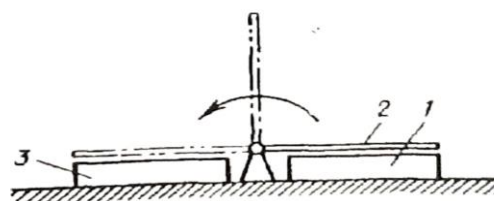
Схема пристрою для складання і зварювання ферм
